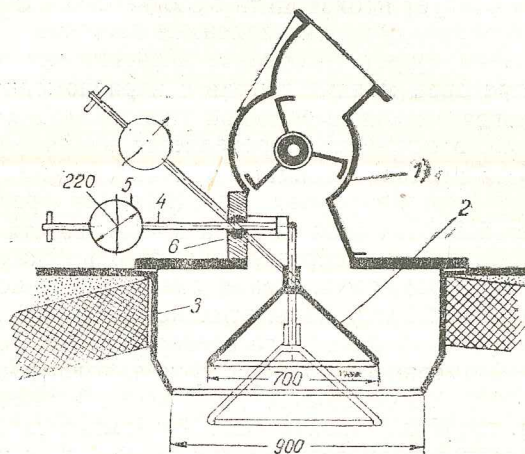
Распределитель топлива: 1 — питатель; 2 — распределительный конус; 3 — отражательное кольцо; 4 — рычаг конуса; 5 — противовес; 6 — шаровой шарнир.
